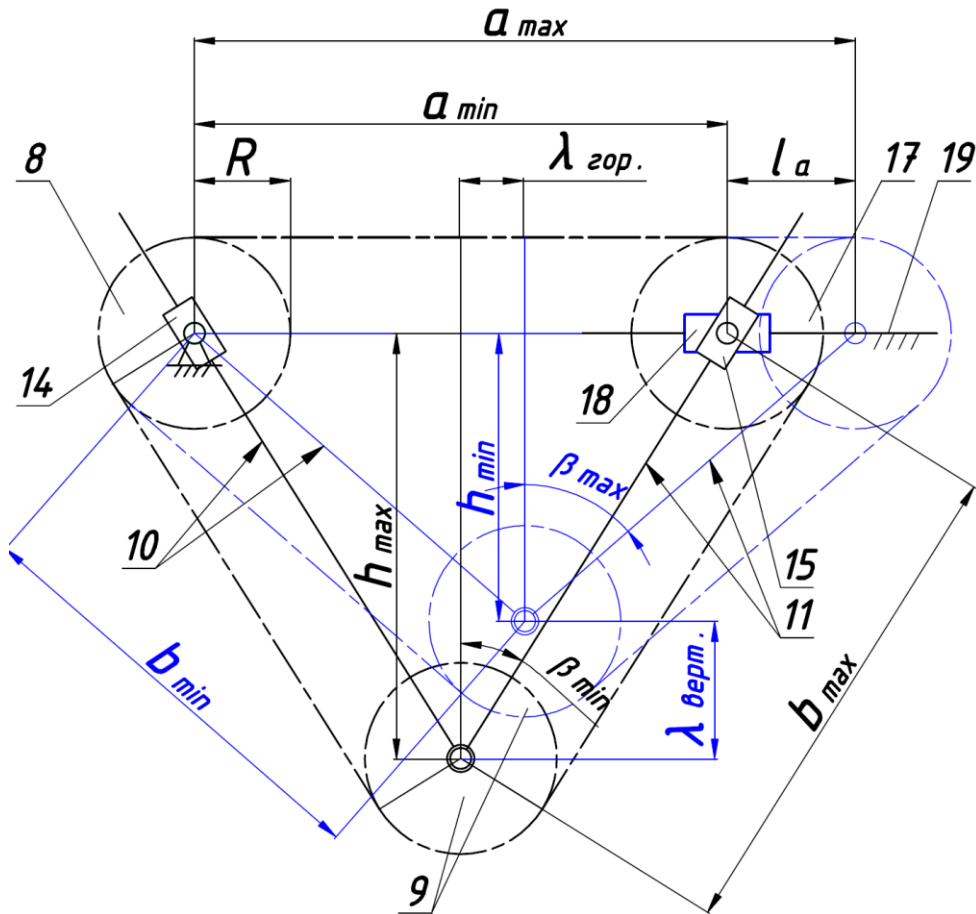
Кінематична схема двохкулісного шарнірного механізму привода машини
